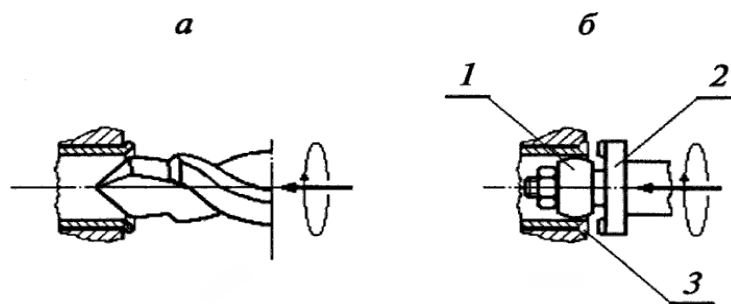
Рассверловка трубы (а). Фрезерование сварного шва (б): 1-направляющая; 2-фреза; 3-сварной шов
